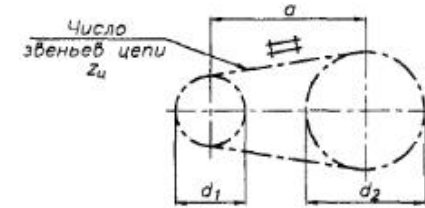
Схема и основные размеры передачи с приводной роликовой (втулочной) цепью
